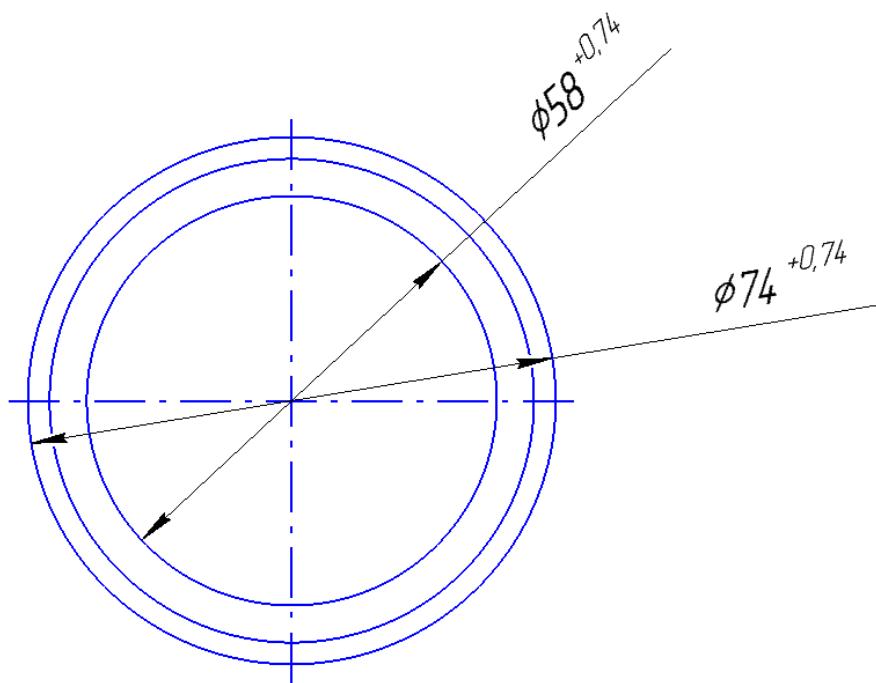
Обработка шлицевых поверхностей червячной фрезой.
